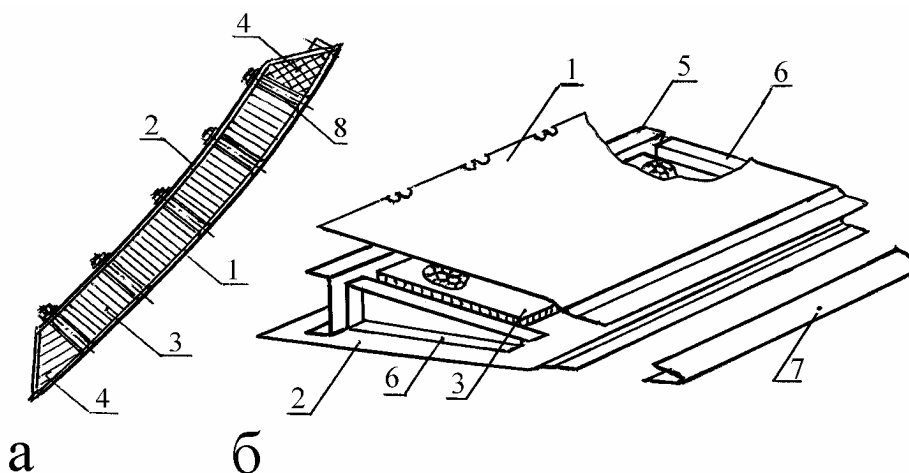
Изделия с применением ПКМ в конструкции самолета Ту-204: а – створка ниши передней опоры шасси; б – интерцептор. 1 – наружная (верхняя) обшивка; 2 – внутренняя (нижняя) обшивка; 3 – наполнитель из сотоблоков; 4 – вкладыш полиуретановый; 5 – лонжерон; 6 – диафрагма; 7 – законцовка; 8 – втулки титановые
